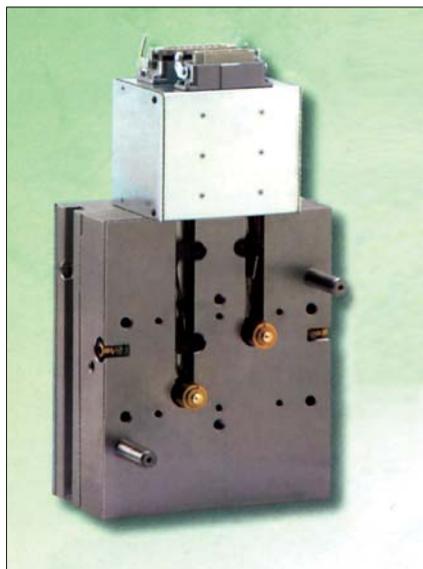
Eco-Smart, da DME, primeiro sistema de câmara quente sob medida para processar o PLA
